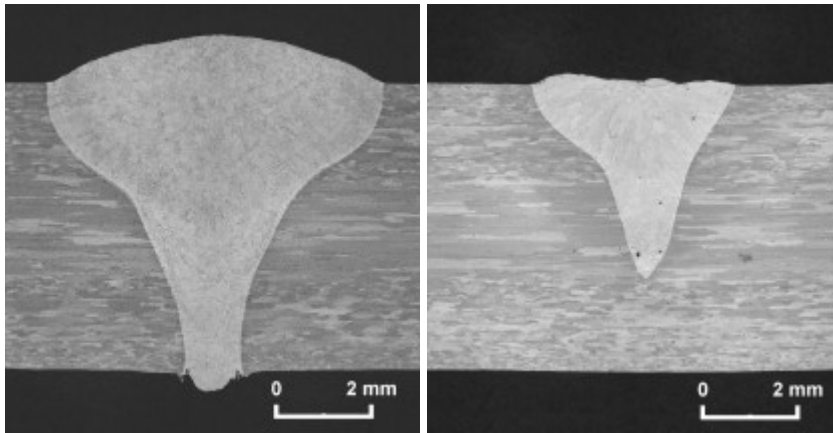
Querschliff einer Laser-MIG-Schweißnaht ($P_L = 6$ kW, $P_{MIG} = 3,6$ kW, $v_S = 2,7$ m/min, Zusatzdraht AlSi12) und einer Laser-Schweißnaht ($P_L = 6$ kW, $v_S = 2,7$ m/min, ohne Zusatzwerkstoff) Blindnaht in AlMgSi1, Blechdicke 6 mm (Ätzmittel: Molybdänsäure)
